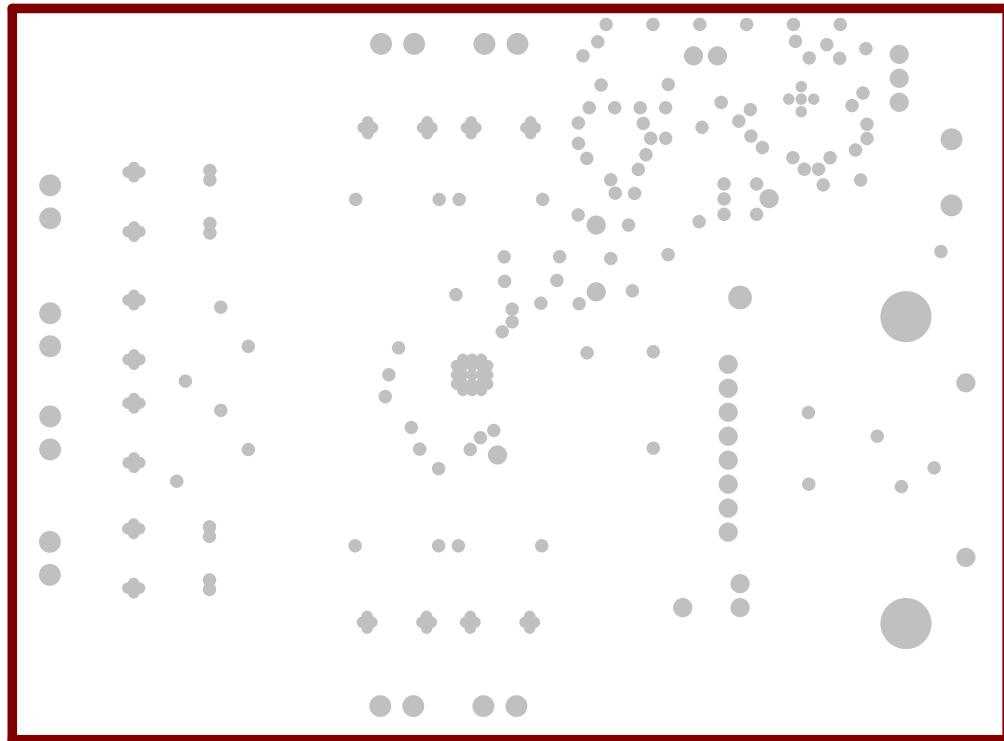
ADS125H18 評価基板 PCB レイアウト — グランド層 2
